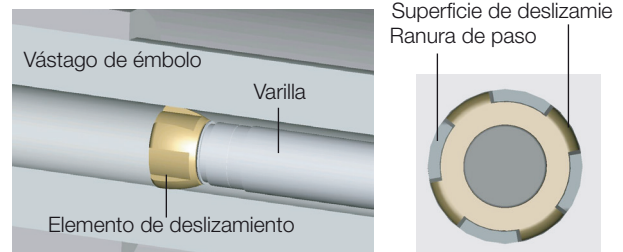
Vista detallada y vista desde arriba del elemento de deslizamiento
